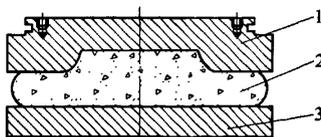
978 齿轮坯缴粗、成形部分轮毂模具结构
